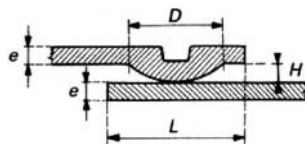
Soudage par bossages : assemblages typiques
